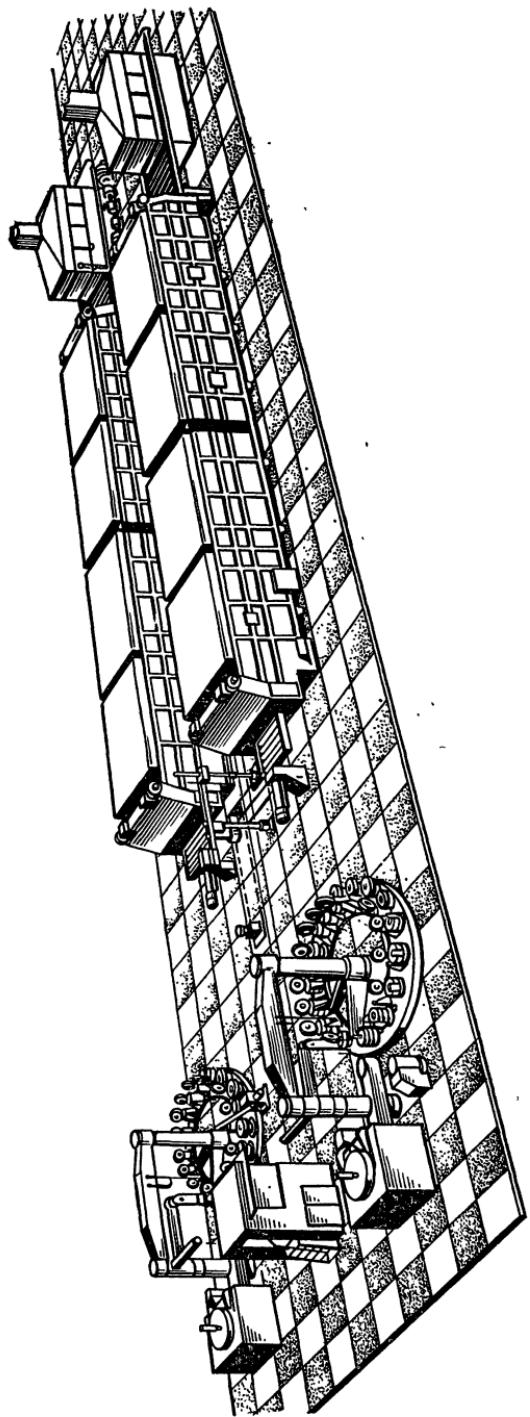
Общий вид комплексно-автоматизированной линии для отливки станции электродвигателя
